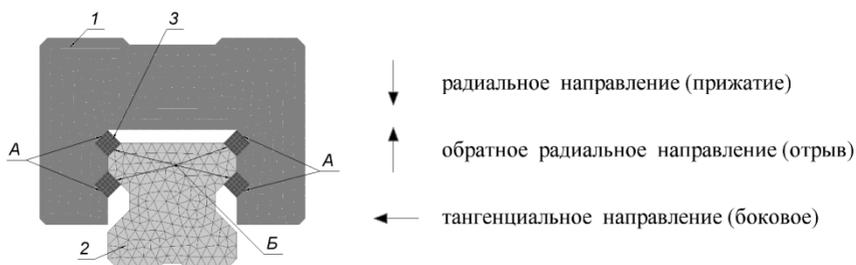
Модель рельсовой направляющей качения: 1 – несущий корпус каретки; 2 – рельс; 3 – тела качения (шарики); А – поверхности взаимодействия тел качения с корпусом каретки; Б – поверхности взаимодействия тел качения с рельсом
